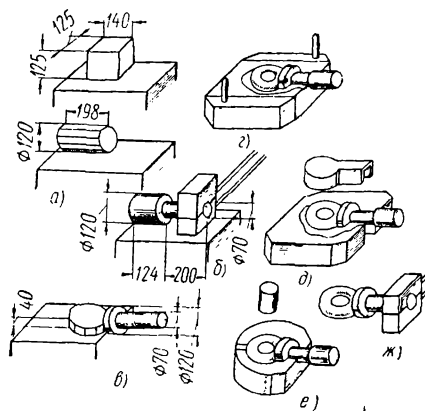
Изготовление поковки рыма: а — ковка заготовки; б — обкатка стержня; в — ковка конца под рым; г — частичная штамповка в подкладном штампе; д — обрезка заусенца; е — пробивка отверстия; ж — окончательная обкатка стержня
